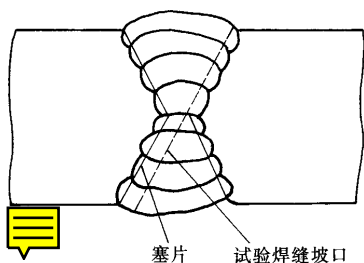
试件间隙的确定和拘束焊缝的焊接
